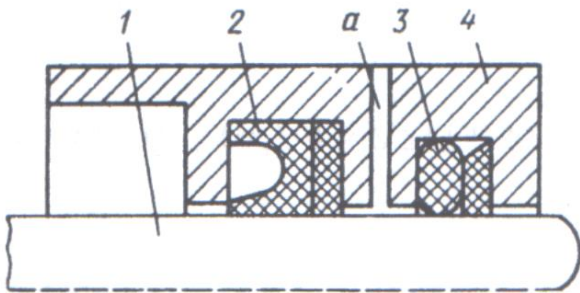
Схема резервування ущільнення штока гідроциліндра
